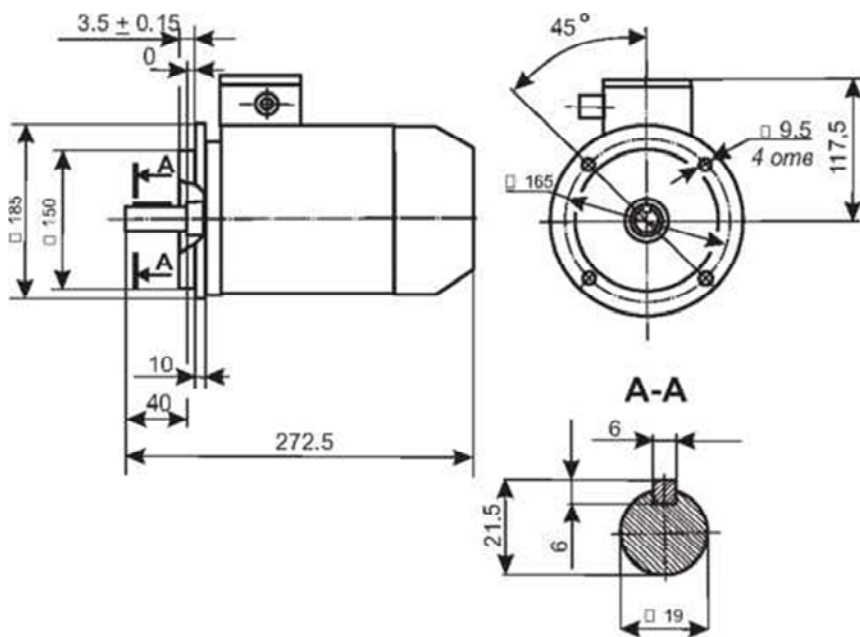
Габаритные размеры двигателей для швейных машин
